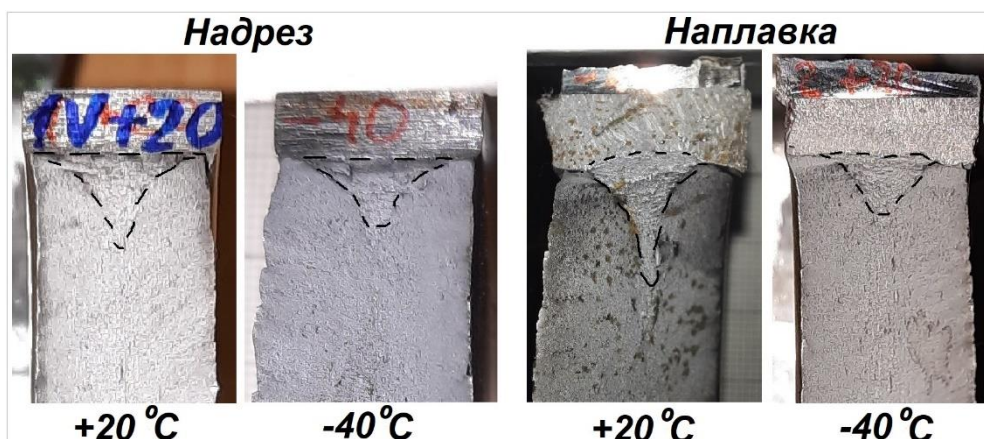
Вид зоны разрушения, примыкающей к концентратору (надрезу/наплавке) для образцов толщиной 15 мм из стали 09ХН3МД.
